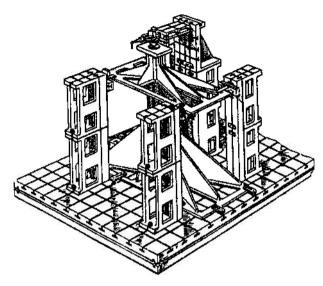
Приспособление для сборки и сварки крупных агрегатов
